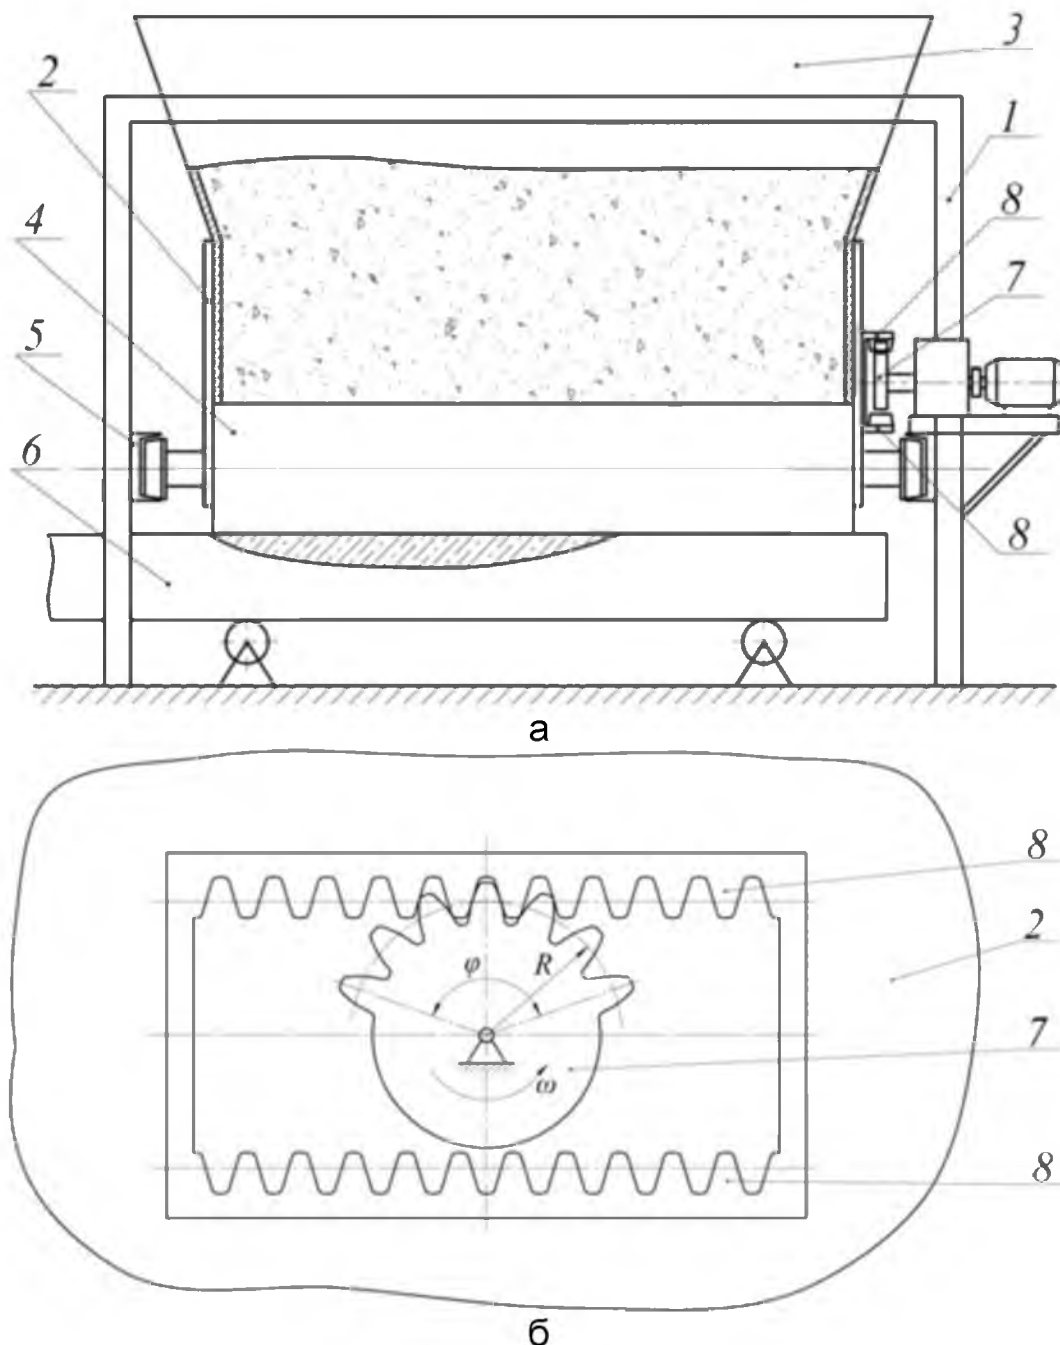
Роликова формувальна установка з приводом від зубчастого сектора (а) та схема приводного механізму (б)
